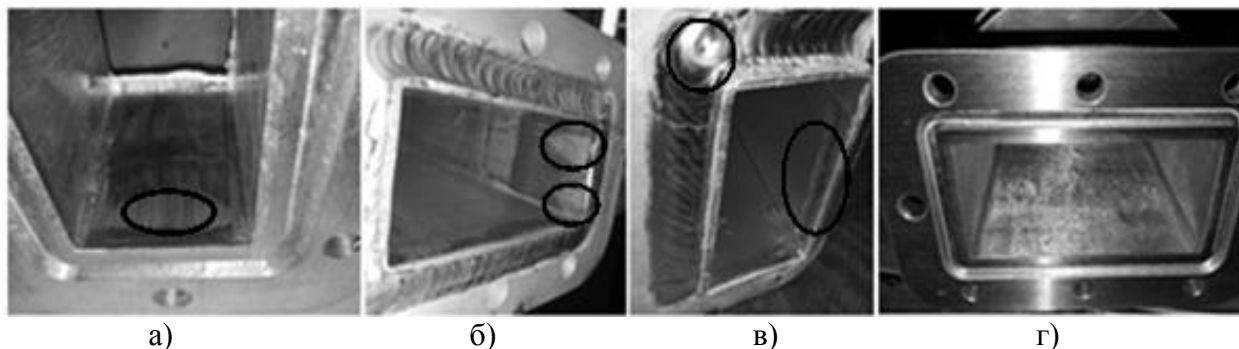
Дефекты сварки волноводов а) вогнутость поверхности б) риски после дорнования в) провар сварного шва г) неоднородная шероховатость обработанной поверхности
